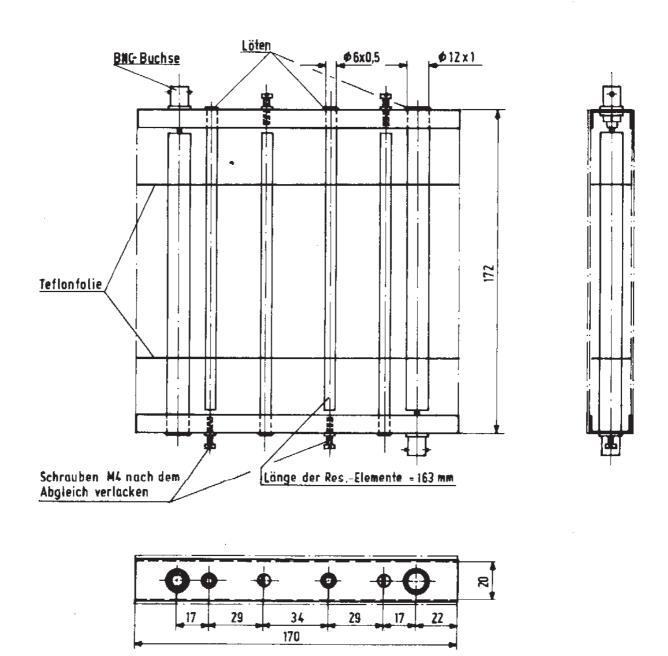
Fingerfilterkonstruktion Einfachbauweise
